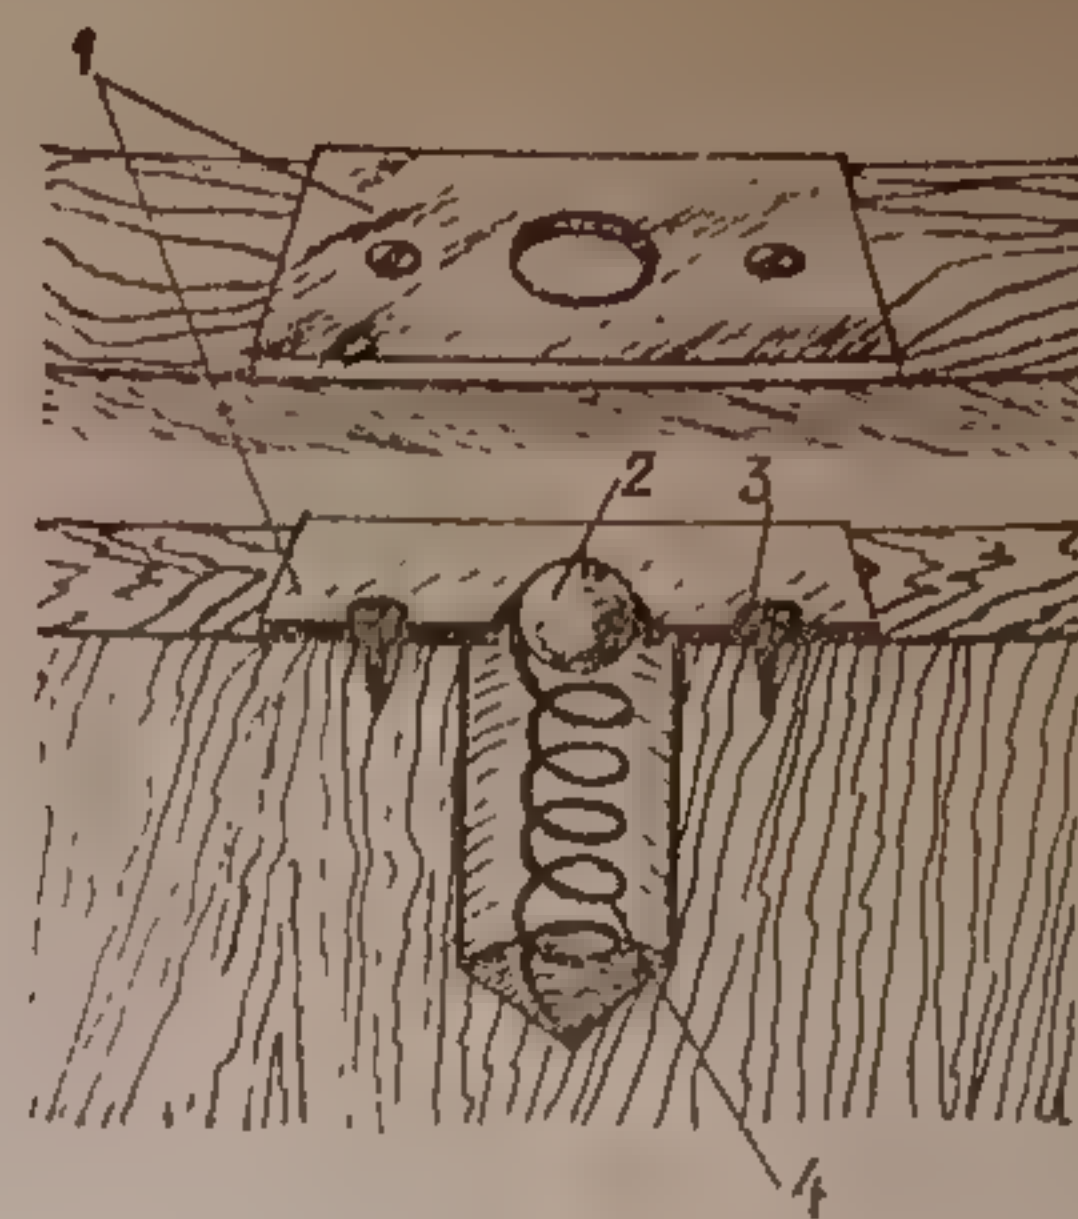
Защелка: 1 — металлические пластины с отверстиями для шарика и шурупов; 2 — шарик; 3 — шурупы; 4 — пружина (верхняя из сопрягаемых деталей для наглядности перевернута)
